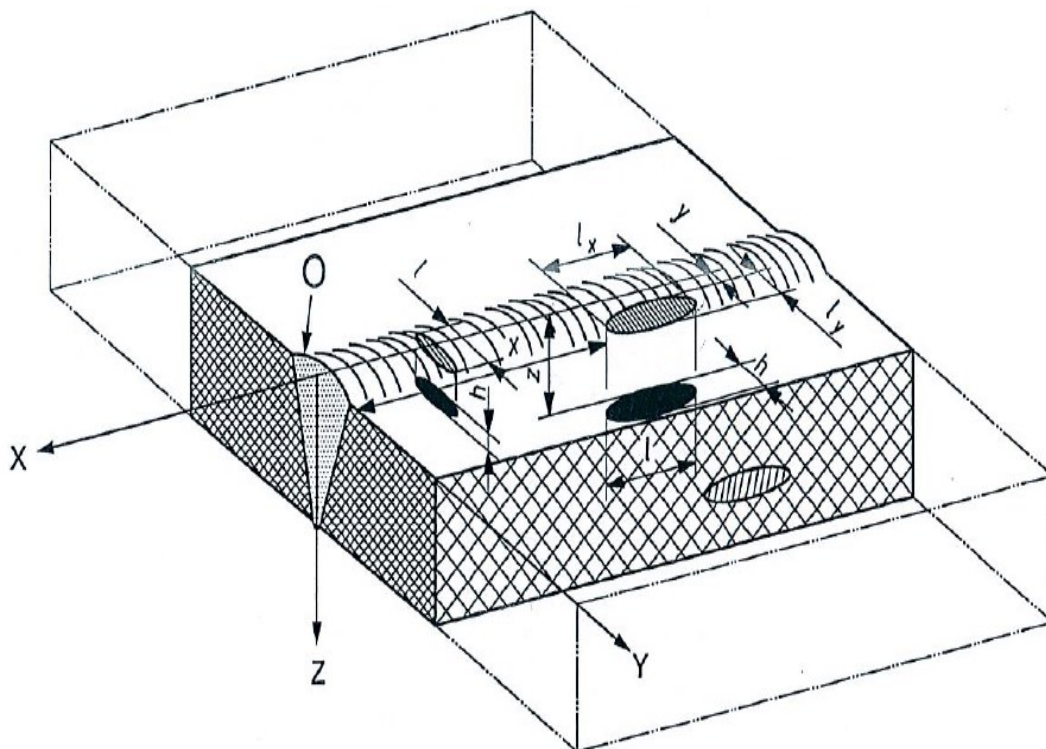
Ultrazvuková skúška vzorky PK13
